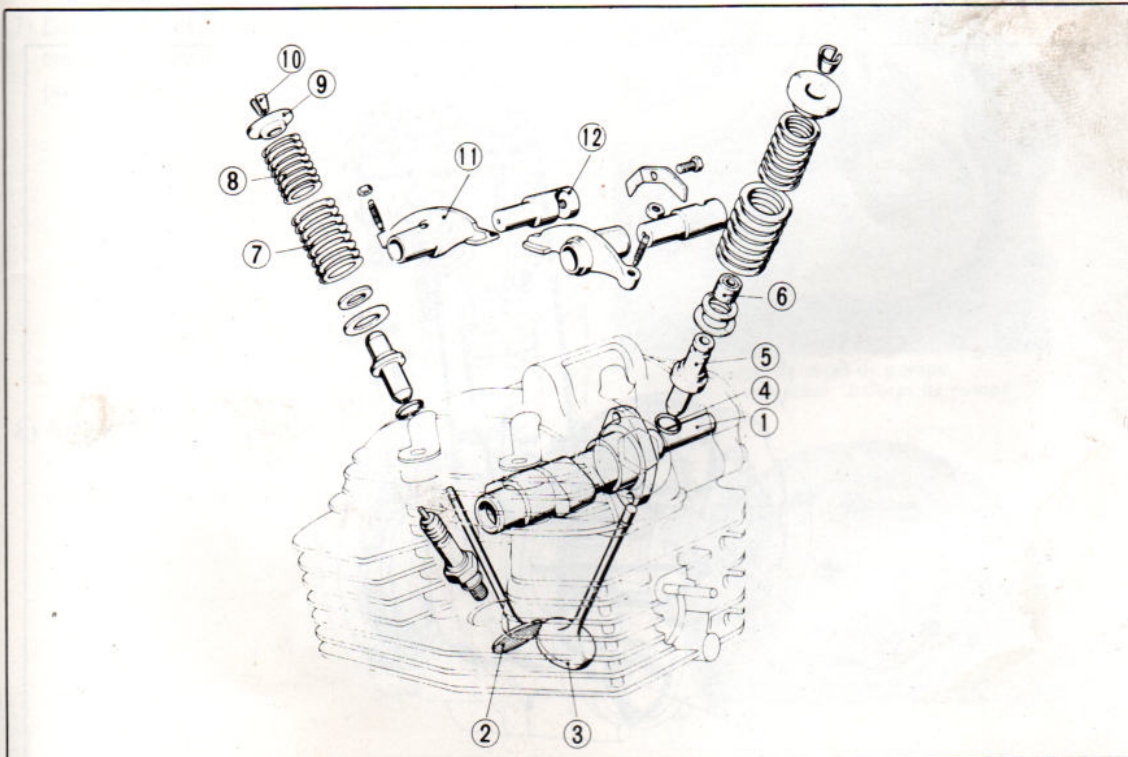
① Arbre à cames ② Soupape d'admission ③ Soupape d'échappement ④ Joint torique ⑤ Guide de soupape
